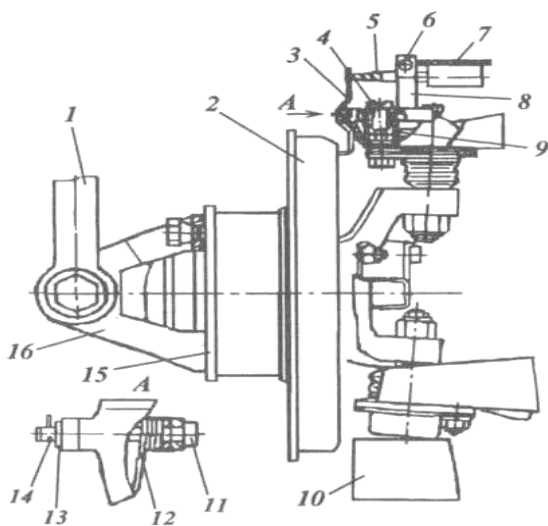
Схема замера зазора в верхних шаровых шарнирах:
